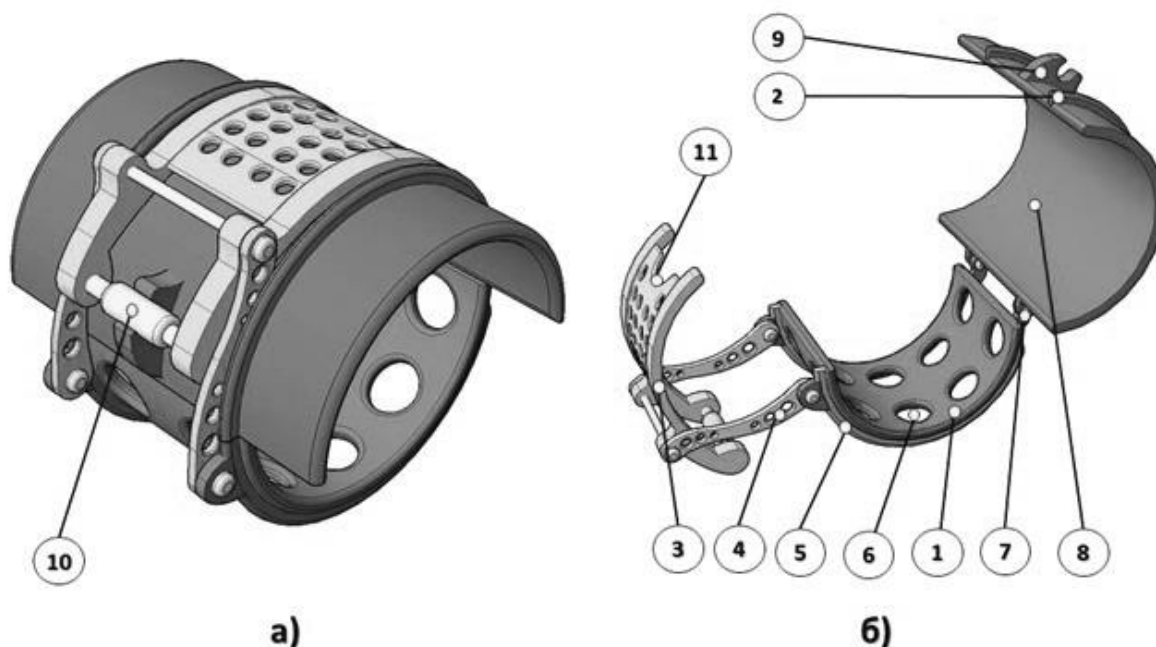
Трехмерная модель конструкции рукавного зажима:
